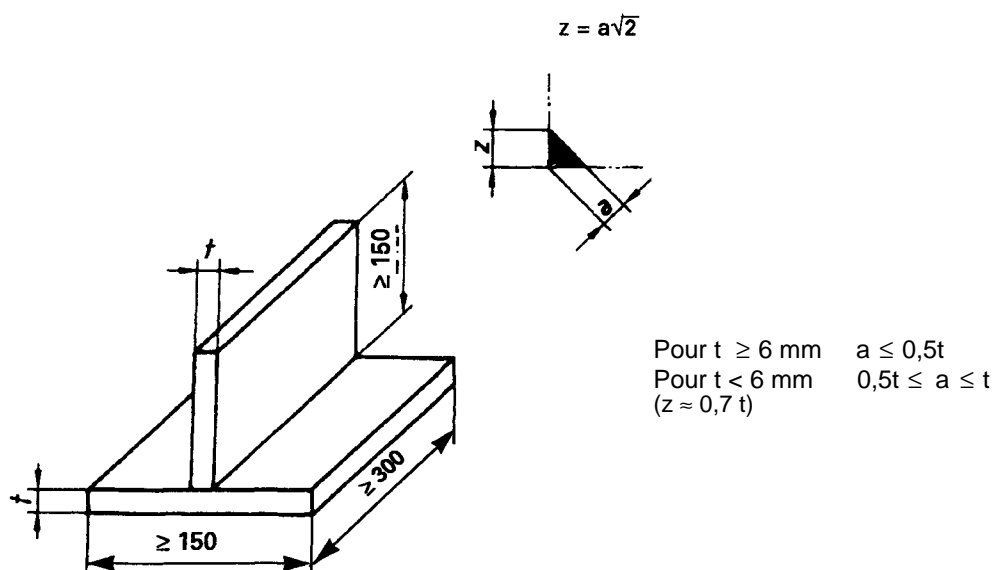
Dimensions de l'assemblage de qualification pour assemblage d'angle de tôles (Dimensions en mm)
